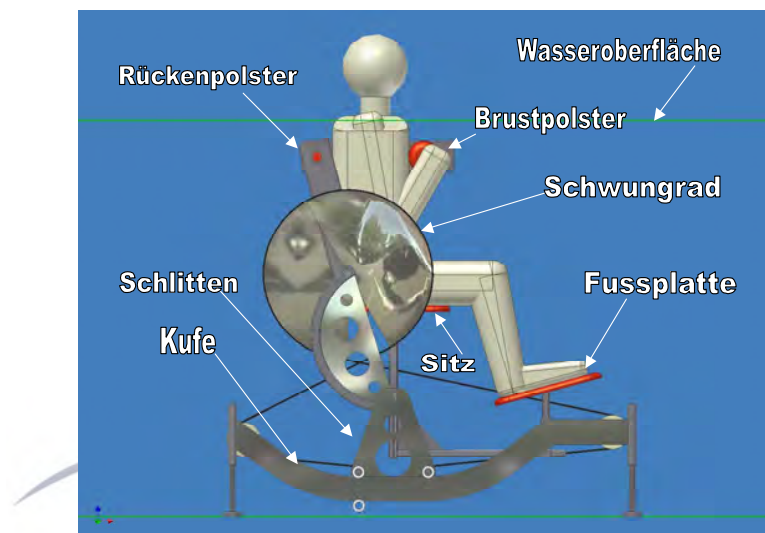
Seitenansicht Prototyp mit Bezeichnungen
